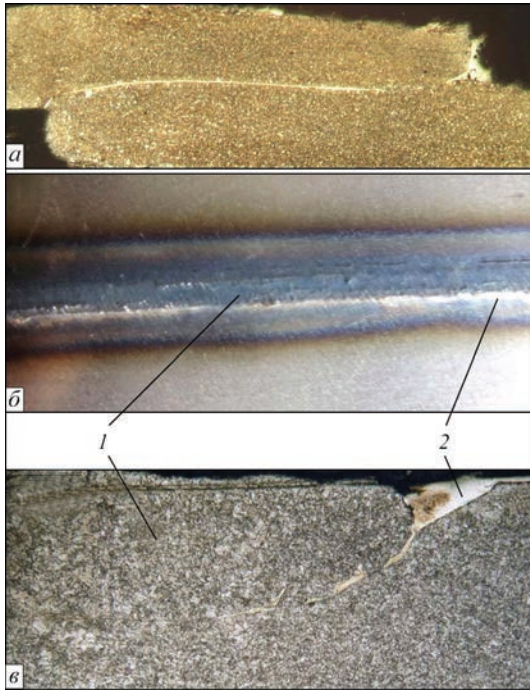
Этапы формирования косостыкового шва на образцах электросварных тонкостенных спиральношовных труб: *a* — поперечное сечение шва на начальном этапе его образования; *б* — внешний вид сформированного сварного соединения (вид сверху); *в* — поперечное сечение сформированного косостыкового шва на конечном этапе; 1 — выдавленный из шва металл, раскатанный по поверхности трубы; 2 — выдавленное из шва активирующее вещество
